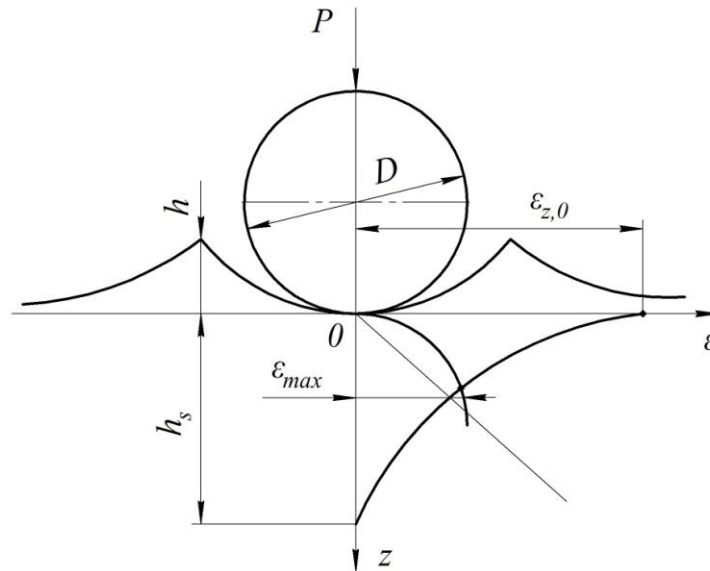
Схема силового контакту інструмента з оброблюваною поверхнею
